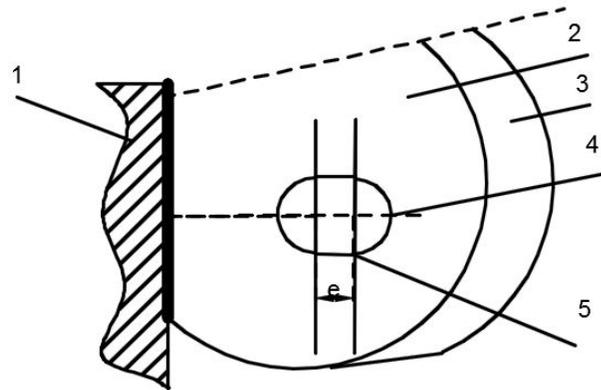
Вариант конструкции рычага с плоской опорной поверхностью; 1- кромка днища; 2- рычаг; 3- захват; 4- паз в захвате; 5- ось рычага; e- эксцентриситет.
